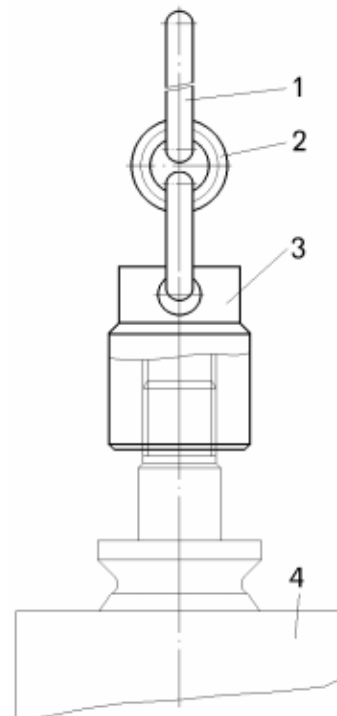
Подвеска для транспортировки цилиндров подвески (резьба на гайке М76х3):
